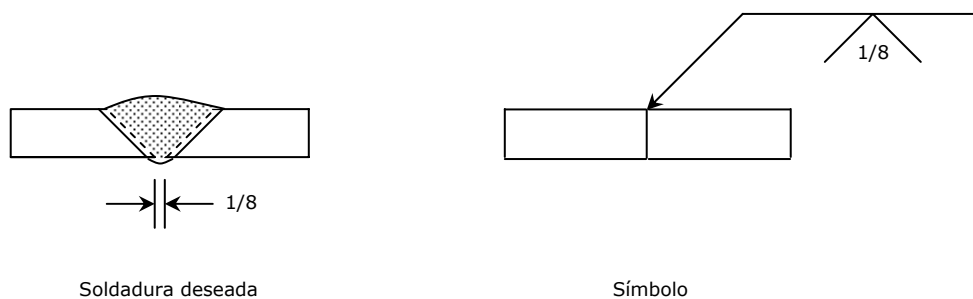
Soldadura de ranura para el lado con flecha
